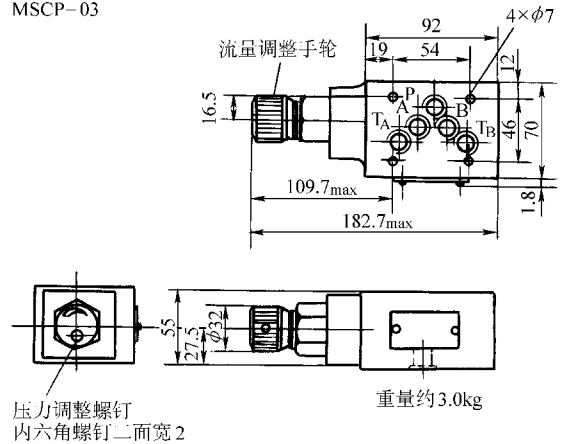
MSCP-03 型叠加式节流阀的外形尺寸
